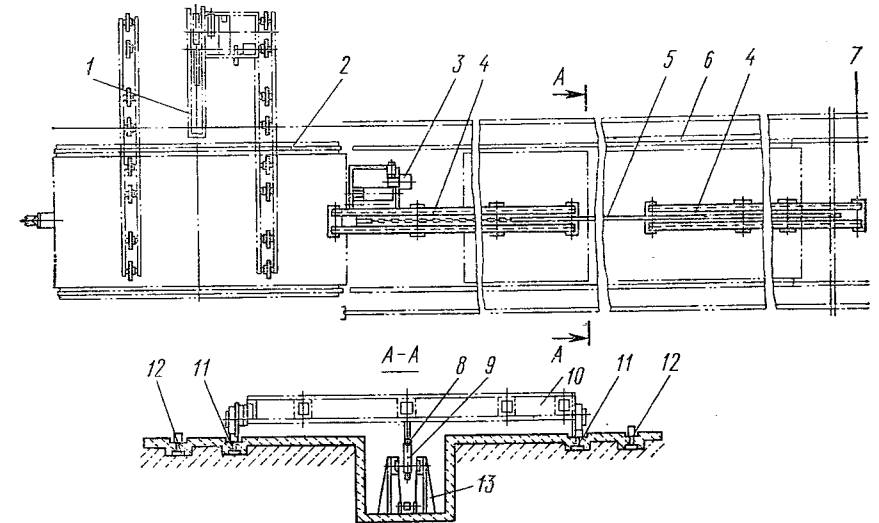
Привод СМЖ-3005Б передвижения форм на конвейерных линиях:
